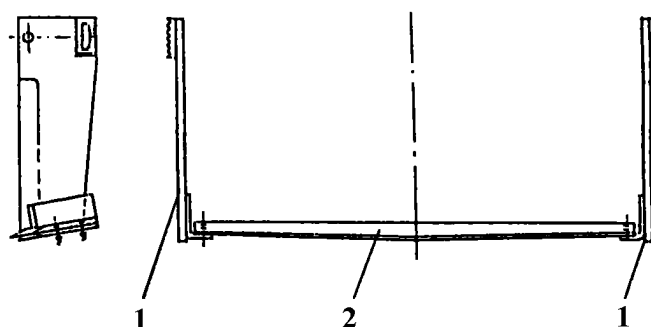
Приспособление ППК-1,2: 1 – стойка; 2 – нож
